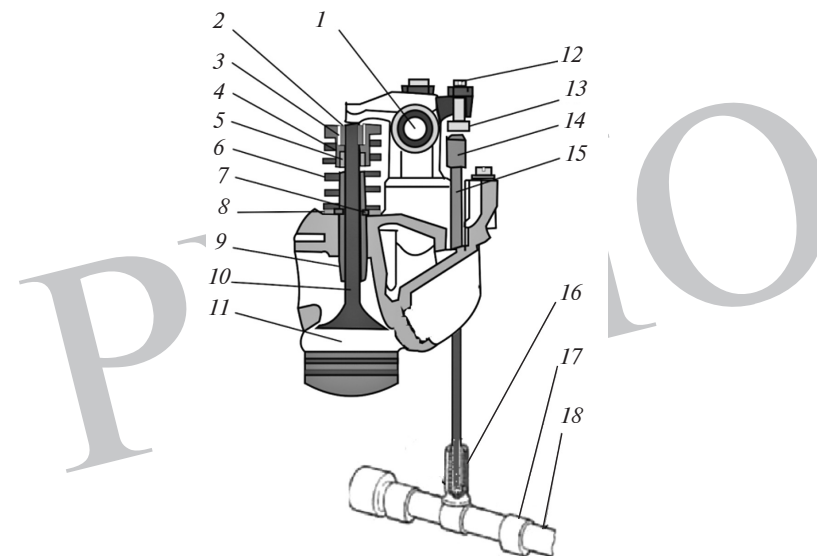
Газораспределительный механизм с подвесными клапанами:
